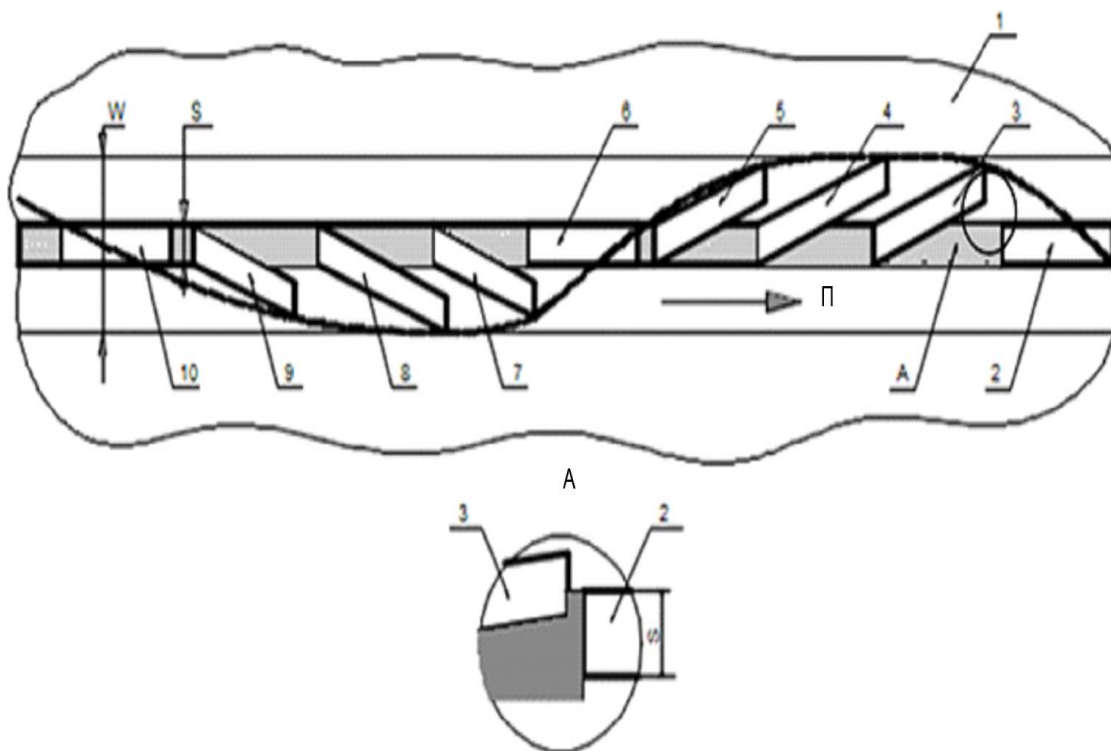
Схема волнообразного расположения зубьев пилы [2]
